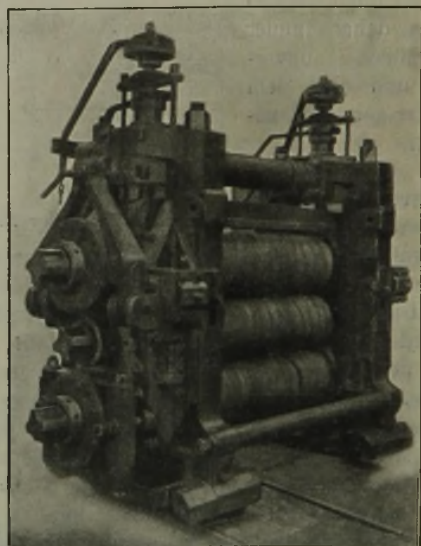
425er-Vorstreck-Triogerüst mit Rollenlagern.
